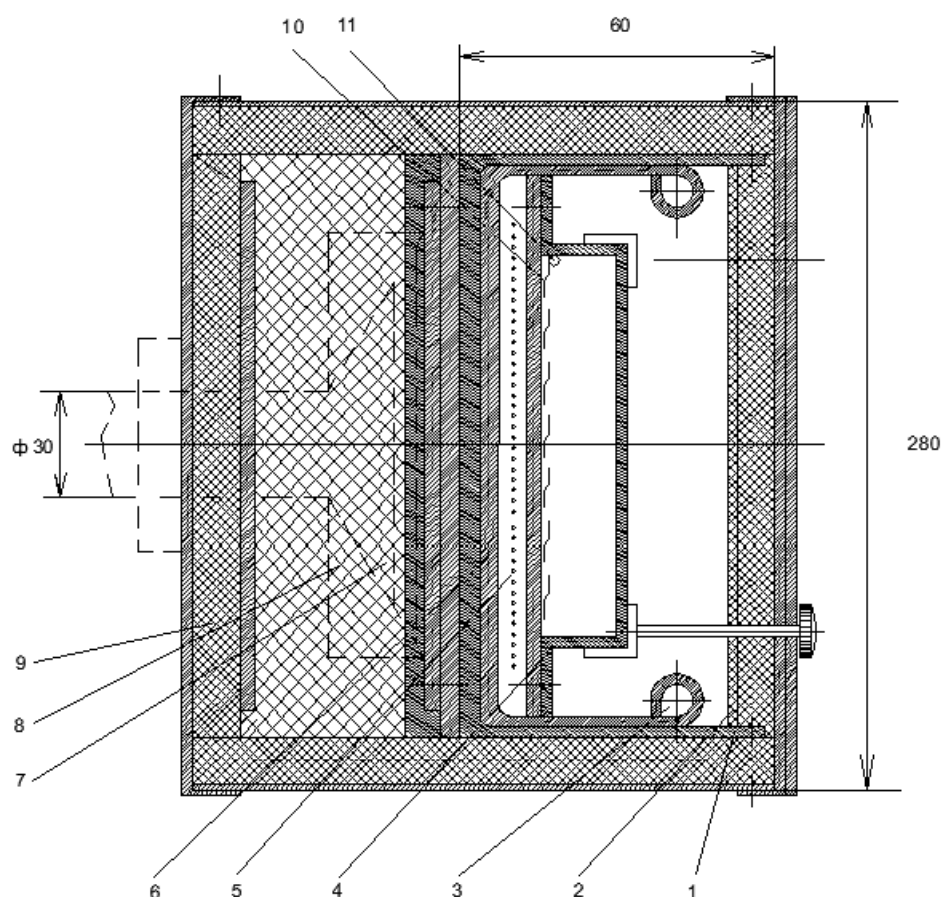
Устройство пористого охлаждения (элемента) (поперечный разрез): 1 – корпус; 2 – крышка; 3 – трубчатая артерия; 4 – вставка; 5 – пористая структура; 6 – электроизоляция (сланца); 7 – основной нагреватель; 8 – охранный нагреватель; 9 – теплоизоляция; 10 – перфорированная прижимная пластина; 11 – микроартерия.
